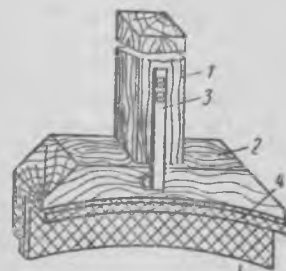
Приспособление для обработки петушков коллектора тягового двигателя НБ-412^М:
